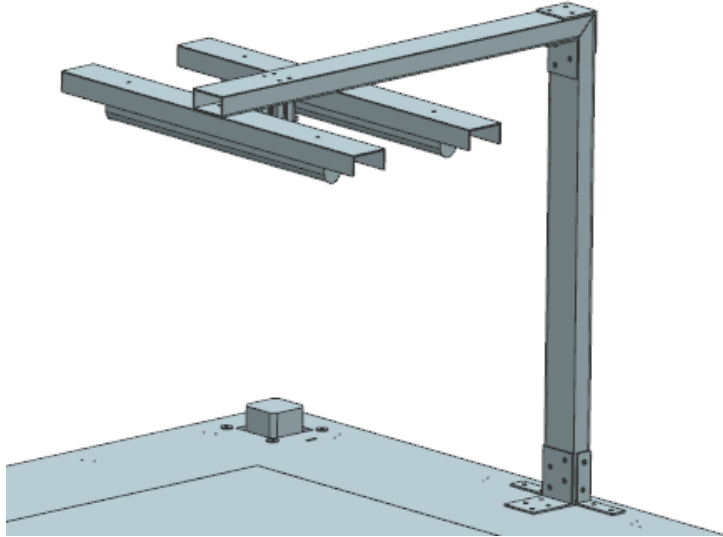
Vista general del diseny 3D de la estructura. (Font: Elaboració pròpia)
